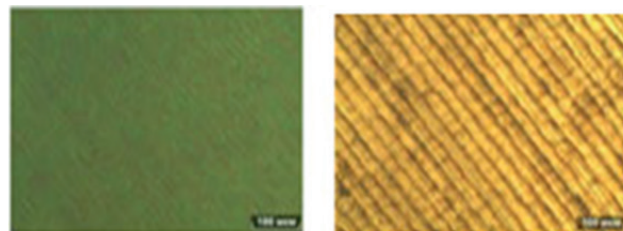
Образцы стали 12X18H10T, обработанные лазерным излучением
